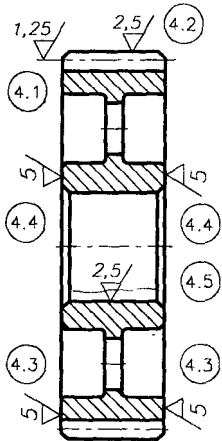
Указание шероховатости поверхностей зубчатого колеса
